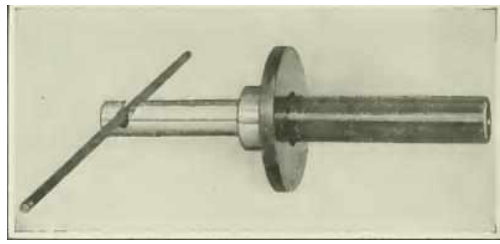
Porta eletrodo para soldagem a arco metálico (Hamilton,1918)
